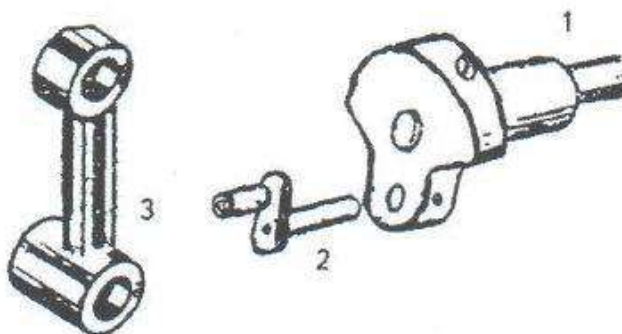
Кривошипно-шатунный механизм: 1-кривошип; 2 - двухколенчатый палец; 3 - шатун
